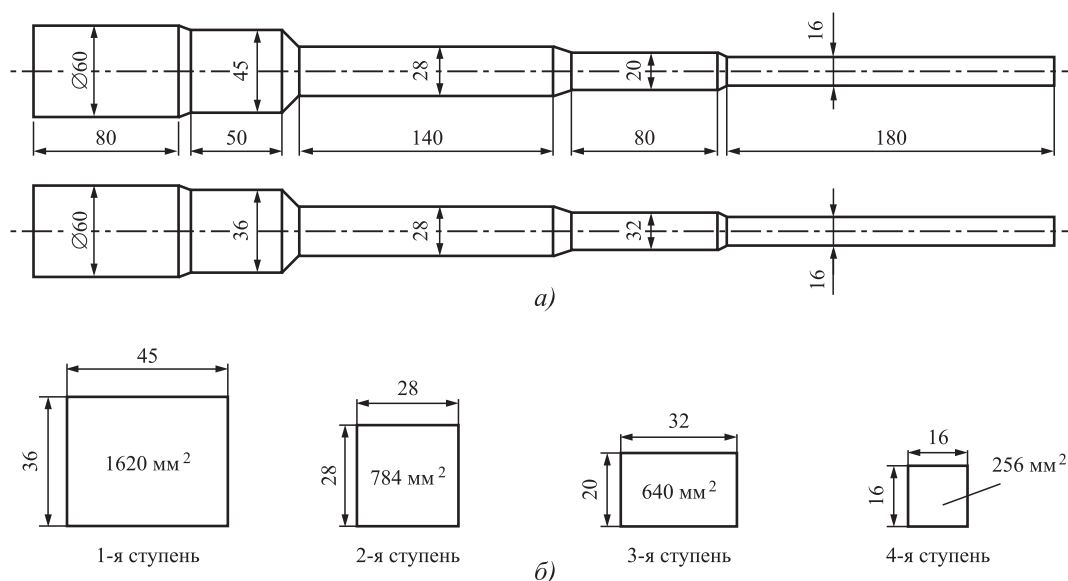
Эскиз ступенчатой поковки (а) и поперечных сечений (б)
